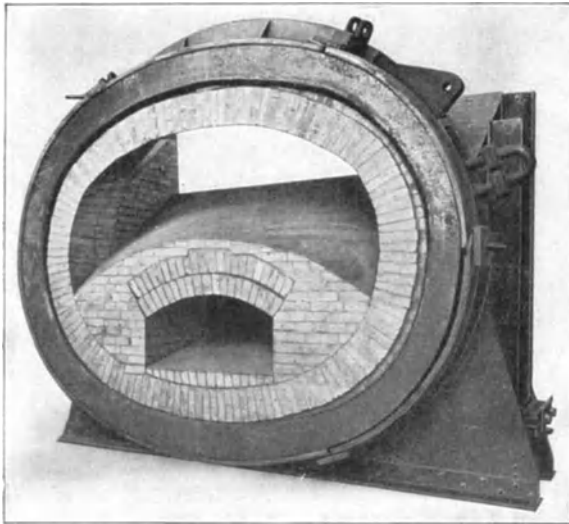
Einsatzstück für den Friedrich-Kopf mit Kühlung.
